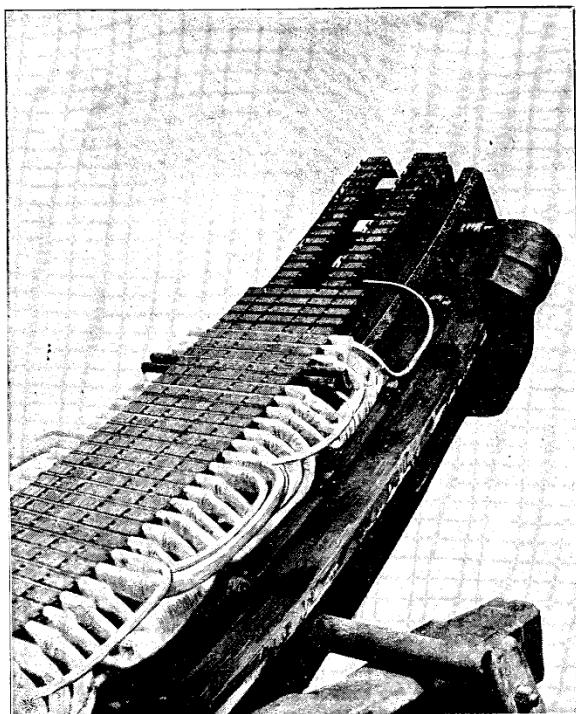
Enroulement de l'induit de l'alternateur Helios.
